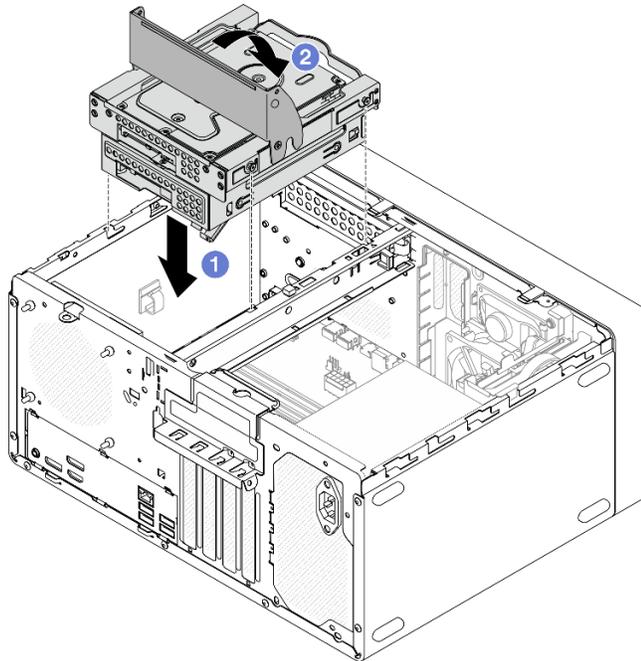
Установка блока отсека для диска отсеков 2 и 3
